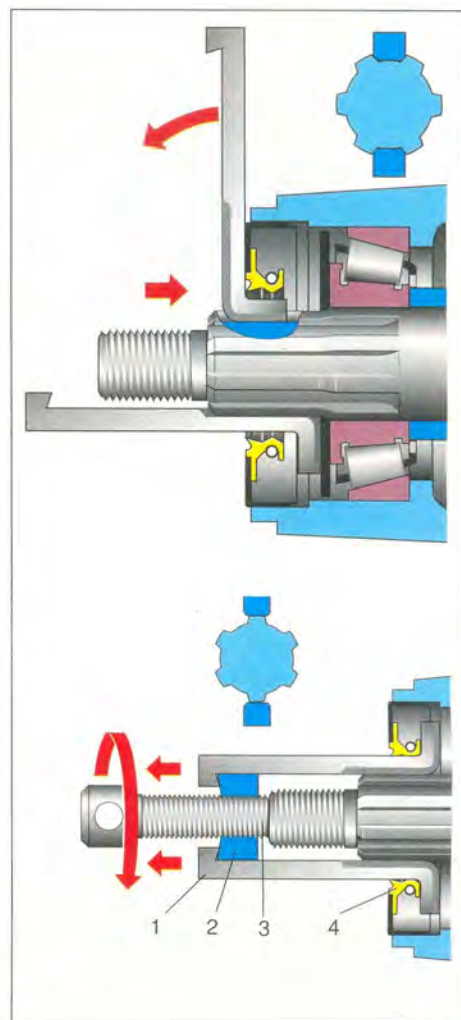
Выпрессовка сальника хвостовика редуктора: 1 — лапка (2шт.); 2 — резьбовая втулка; 3 — винт; 4 — сальник.
